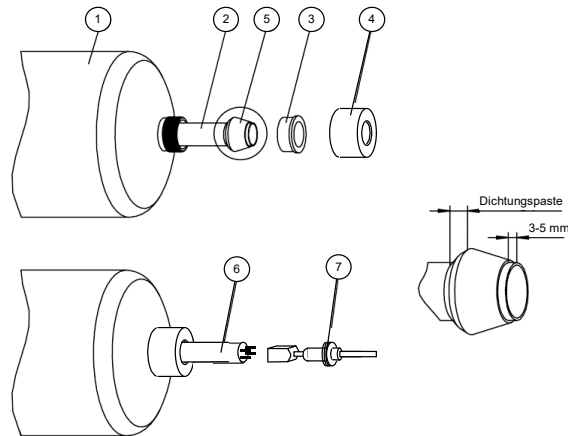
Plan de montage UV 60 S – UV 200 S
